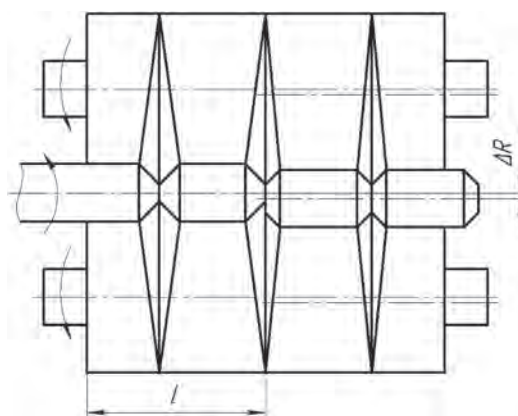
Сборный инструмент для разделения прутков поперечно-клиновой прокаткой
